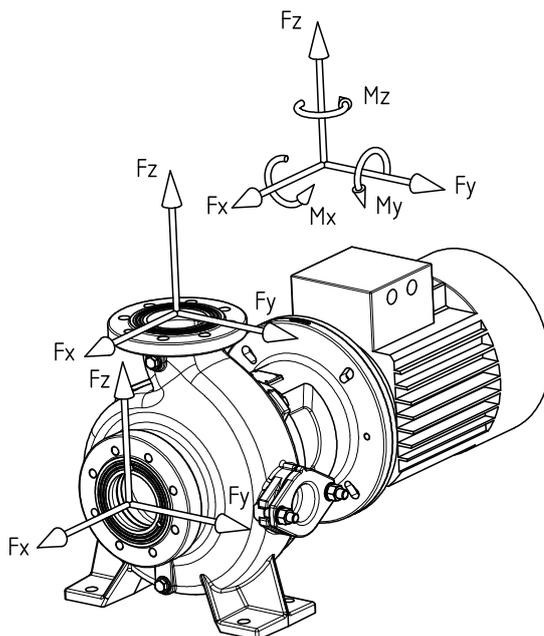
Fuerzas y pares en las bocas de la bomba, montaje horizontal
